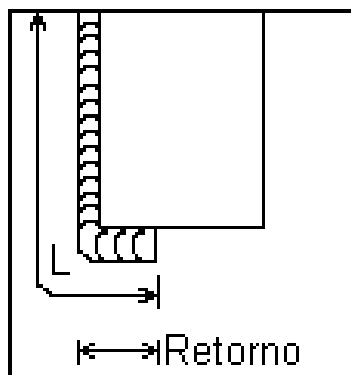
Simbología para Uniones Soldadas AWS.
